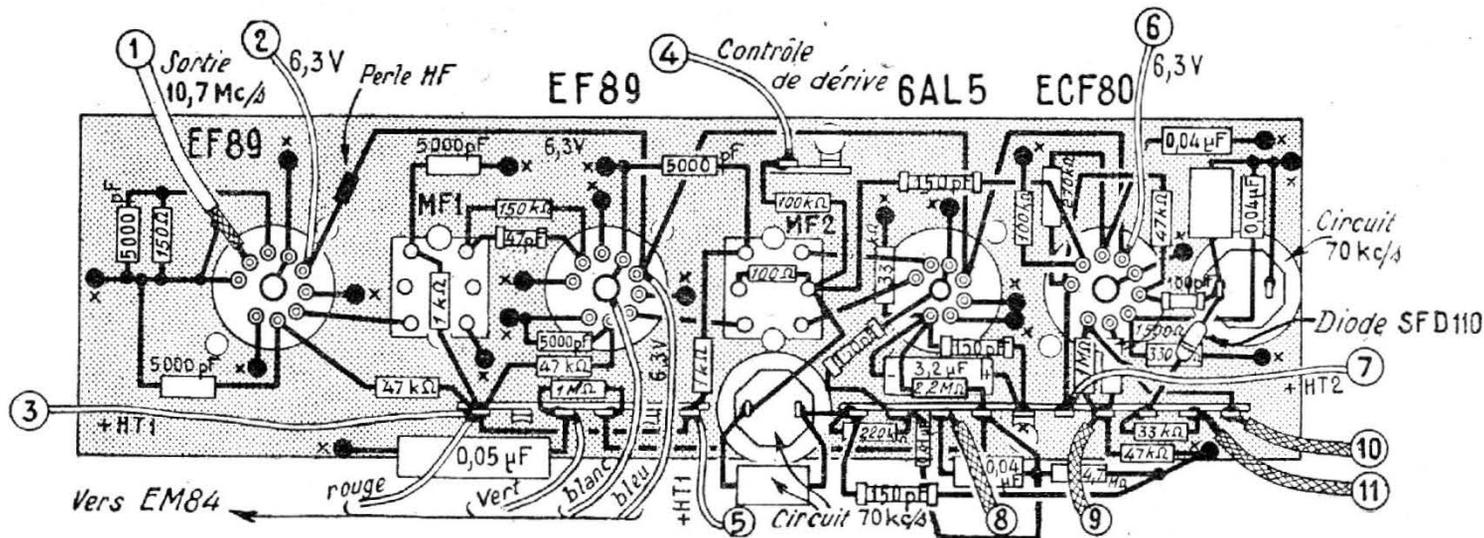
Câblage de la partie inférieure du côté arrière du châssis.
